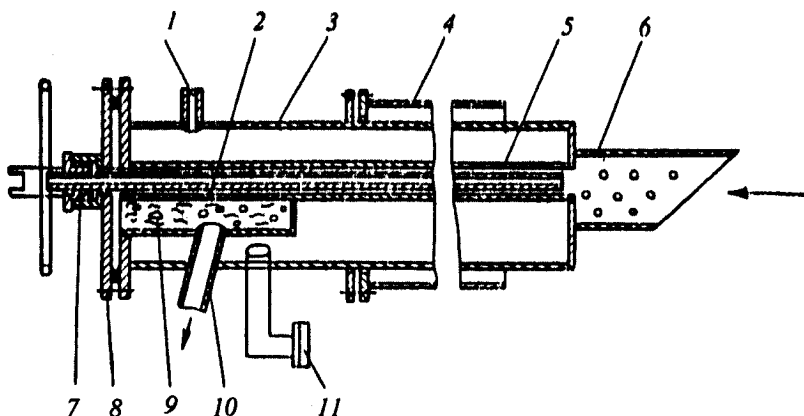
Конструкція пробовідбірника газоаналізатора
